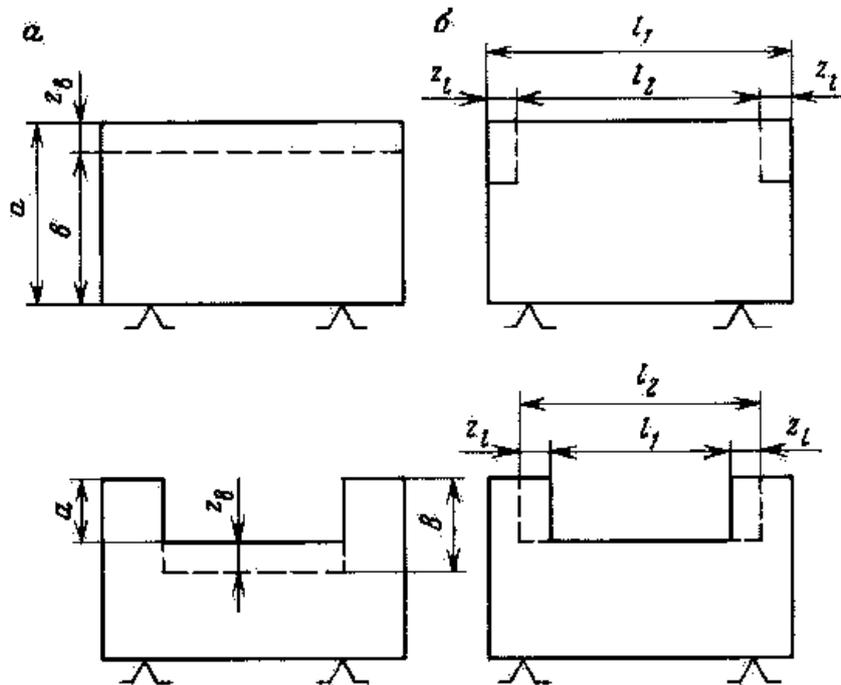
Схемы расположения промежуточного (а) и симметричного (б) припусков для наружных и внутренних поверхностей заготовок где z_b - промежуточный припуск, мм; a - исходный размер заготовки, мм; b - размер заготовки после выполнения технологического перехода, мм.
